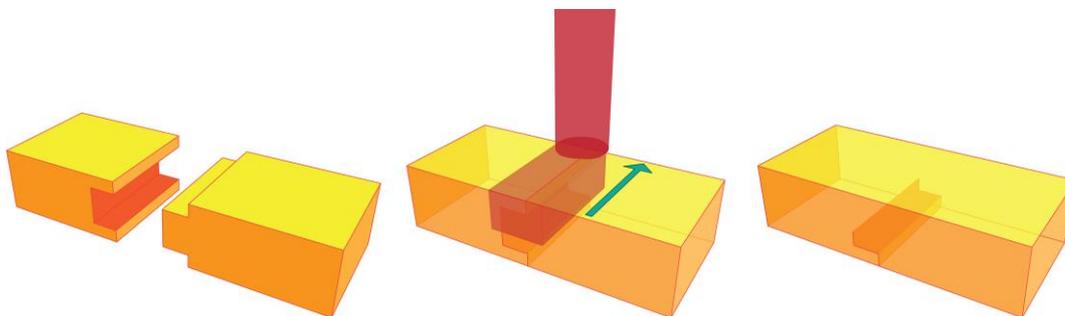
Esquema de soldagem a frio por laser demonstrando o aquecimento e fundição de um pequeno encaixe.
